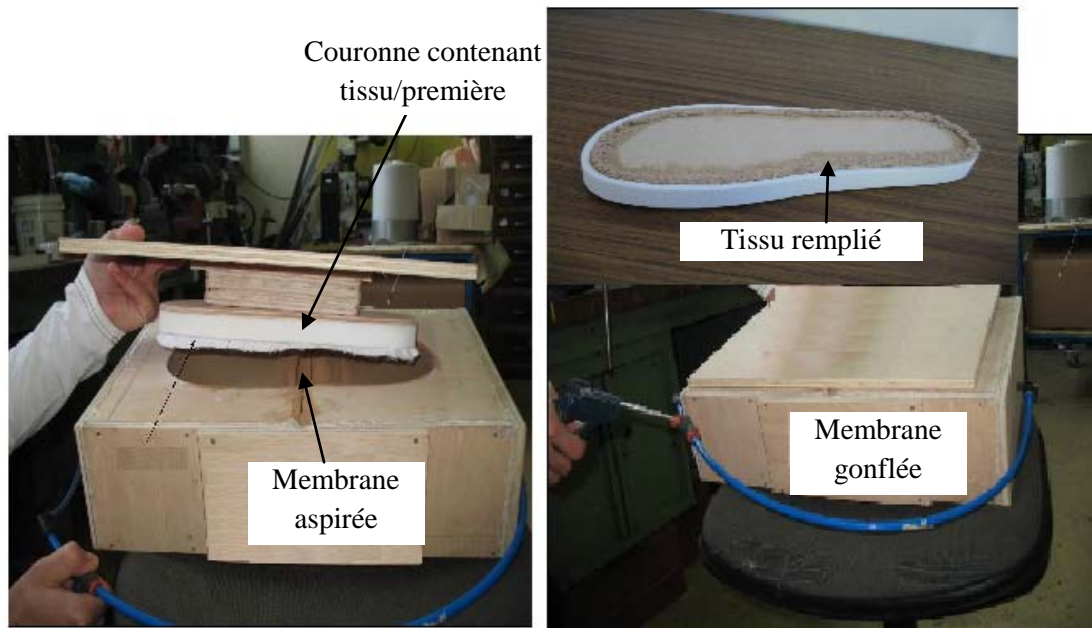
Principe de remplissage de première mousse : prototype réalisé
